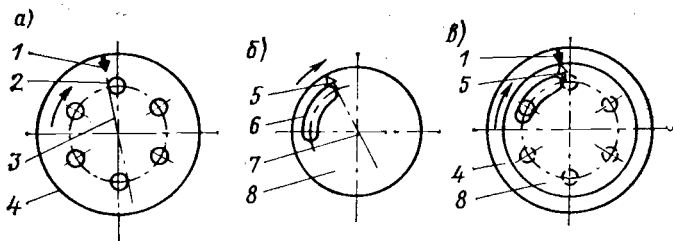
Проверка дискового воздухораспределителя: а — корпус распределителя; б — диск распределителя; в — диск с корпусом в сборе
